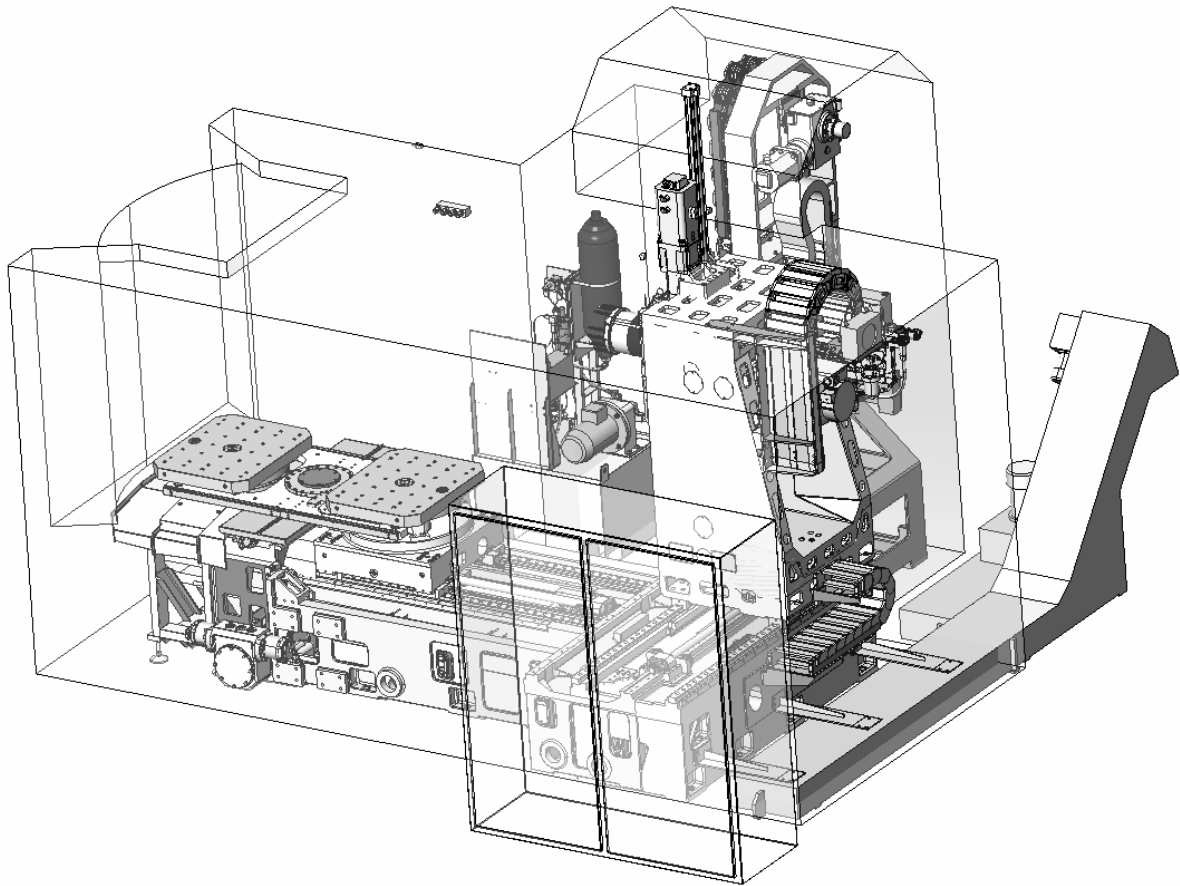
Конструкторская 3D-модель обрабатывающего центра
